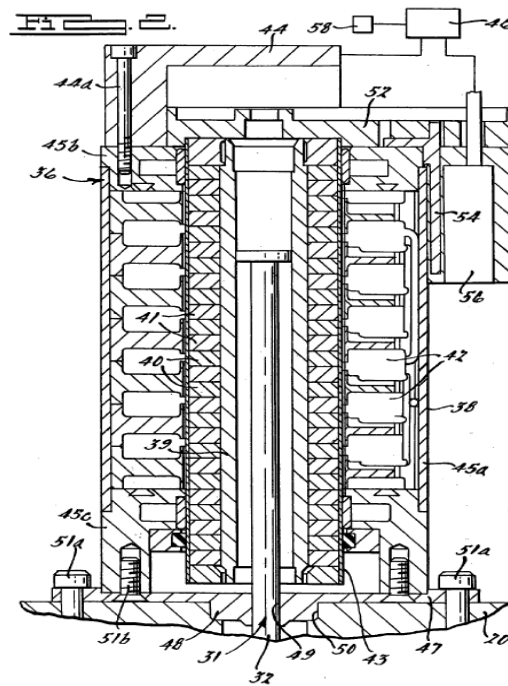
Disegno della bobina brevettata per muovere lo spillo dell'otturatore.
